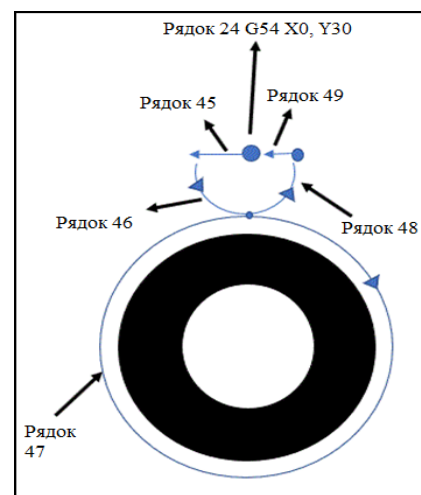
Траєкторія руху інструменту при обробці порожнистого циліндру
